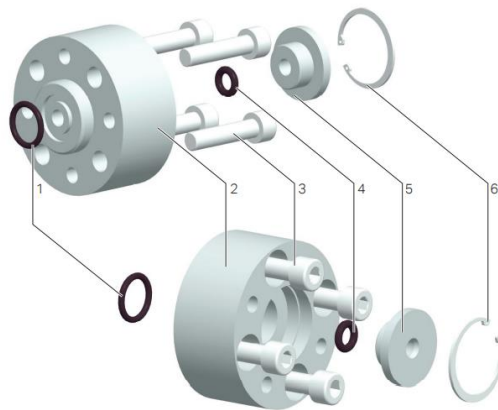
Despiece detallado para desensamblar el sujetador del inyector.
